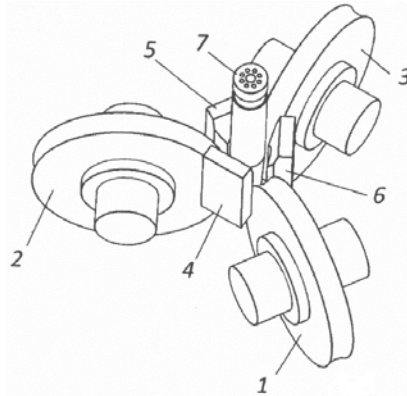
Загальний вигляд пристрою для валкової розливки-прокатки суцільних та порожнистих тіл
